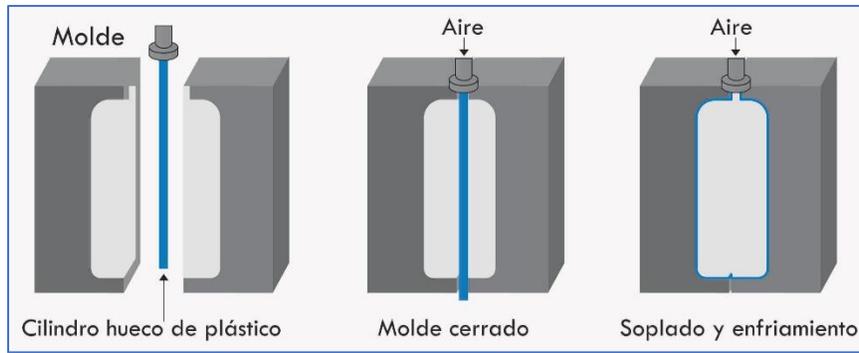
Técnica de moldeo de plástico a baja presión (soplado)
